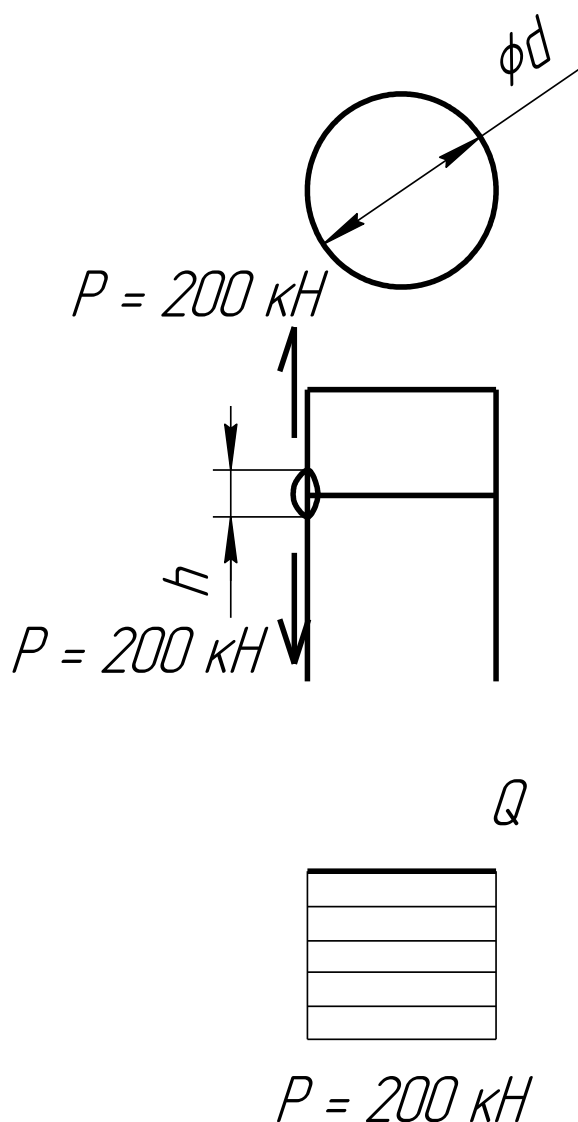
Для расчета сварного шва гидравлического цилиндра
